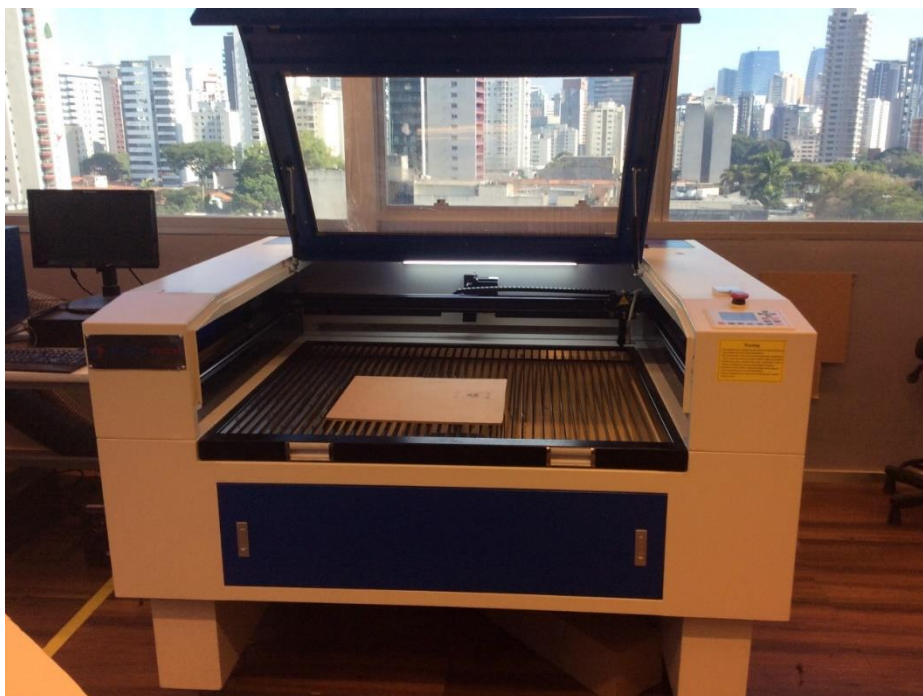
Cortadora com tampa aberta (Fonte: própria)
